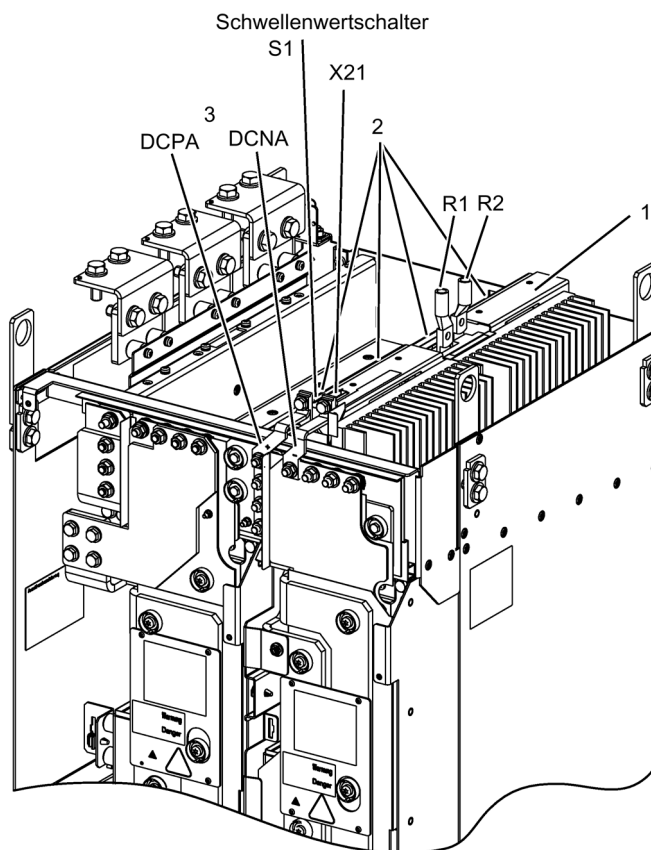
Montage des Braking Module in ein Power Module Bauform HX
